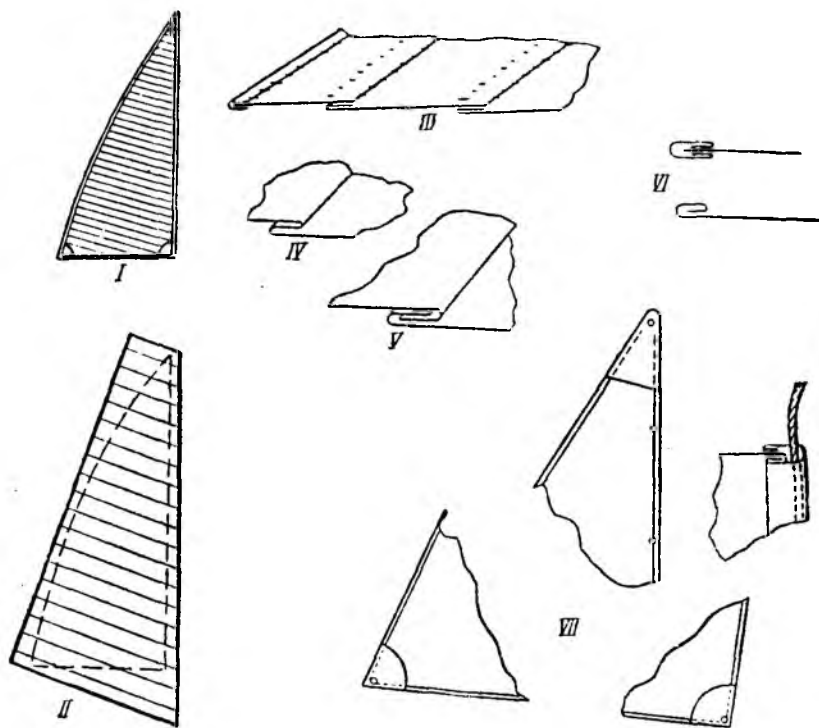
I — направление складок-швов на парусе; II — обчерчивание выкройки; III — складки и накладной рубец; IV — деталь складки; V — шов; VI — деталь рубца; VII — канавки и шнурок по передней шкесторине.
